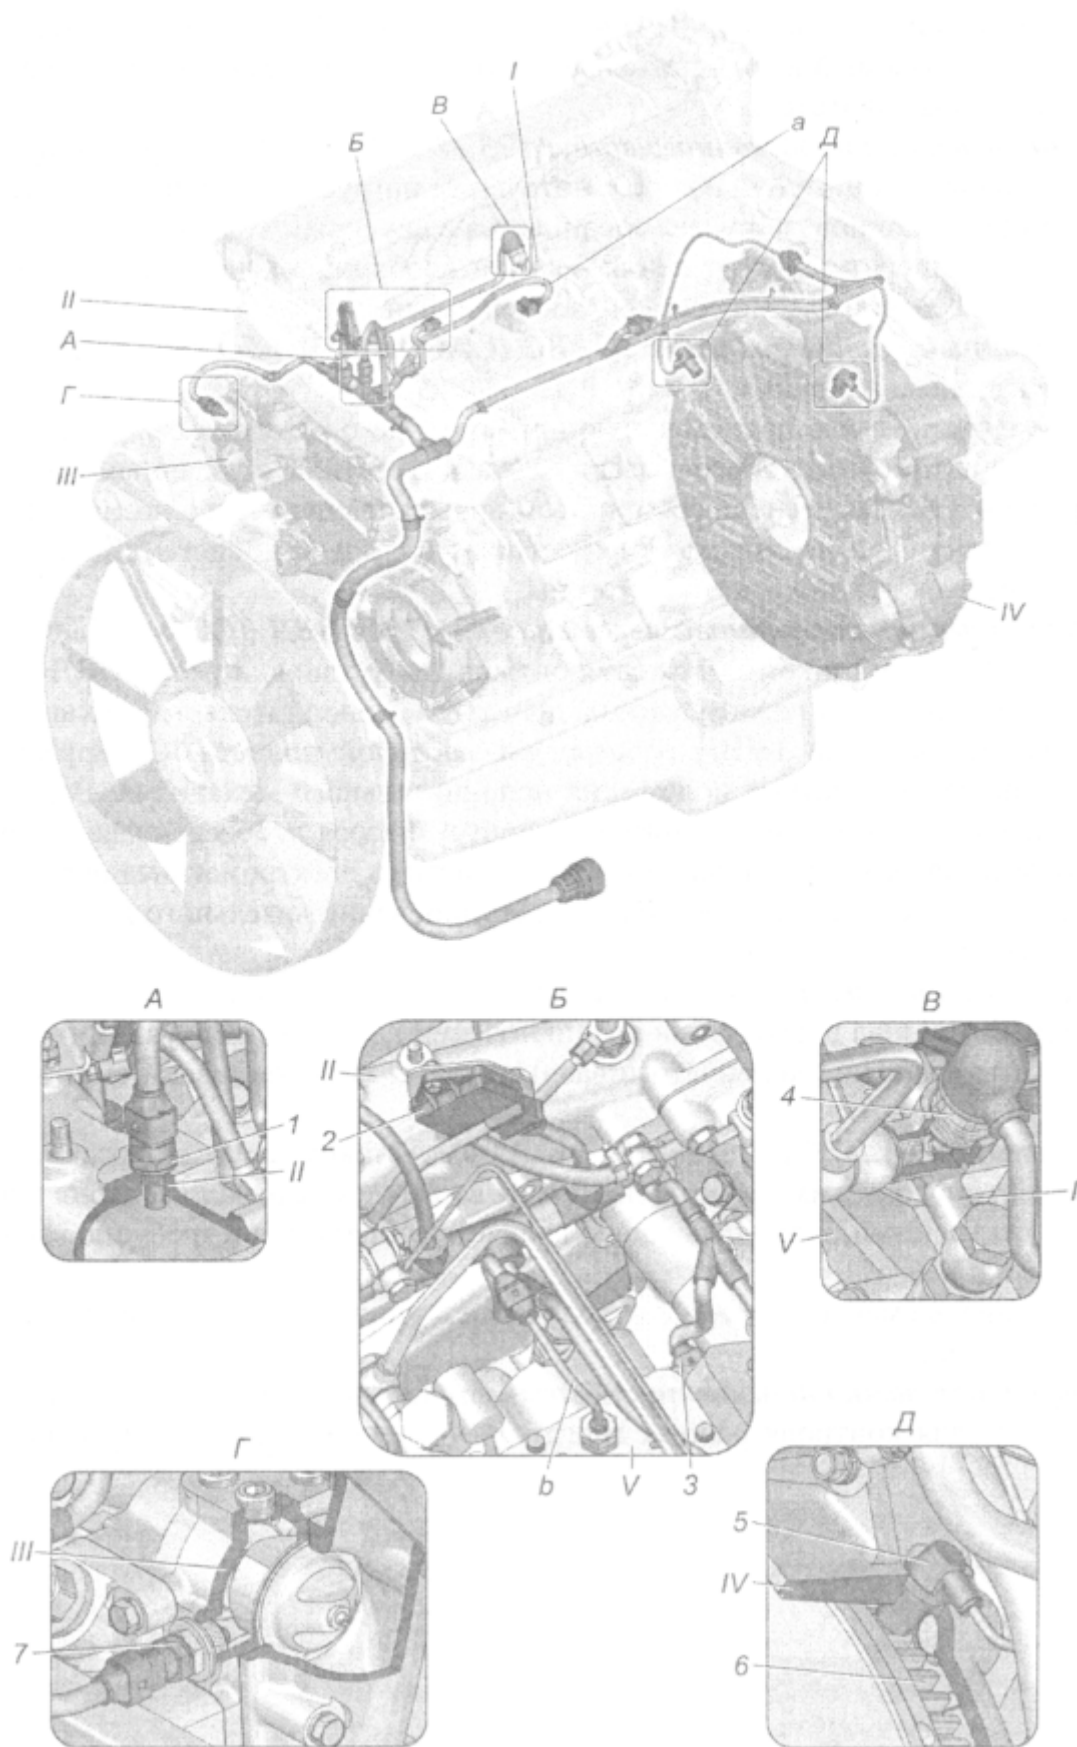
Установка жгута проводов на двигателе с V-образным ТНВД «ЯЗДА»: I - корпус клапана; II - патрубок соединительный; III - корпус водяных каналов; IV - картер маховика; V - топливный насос
